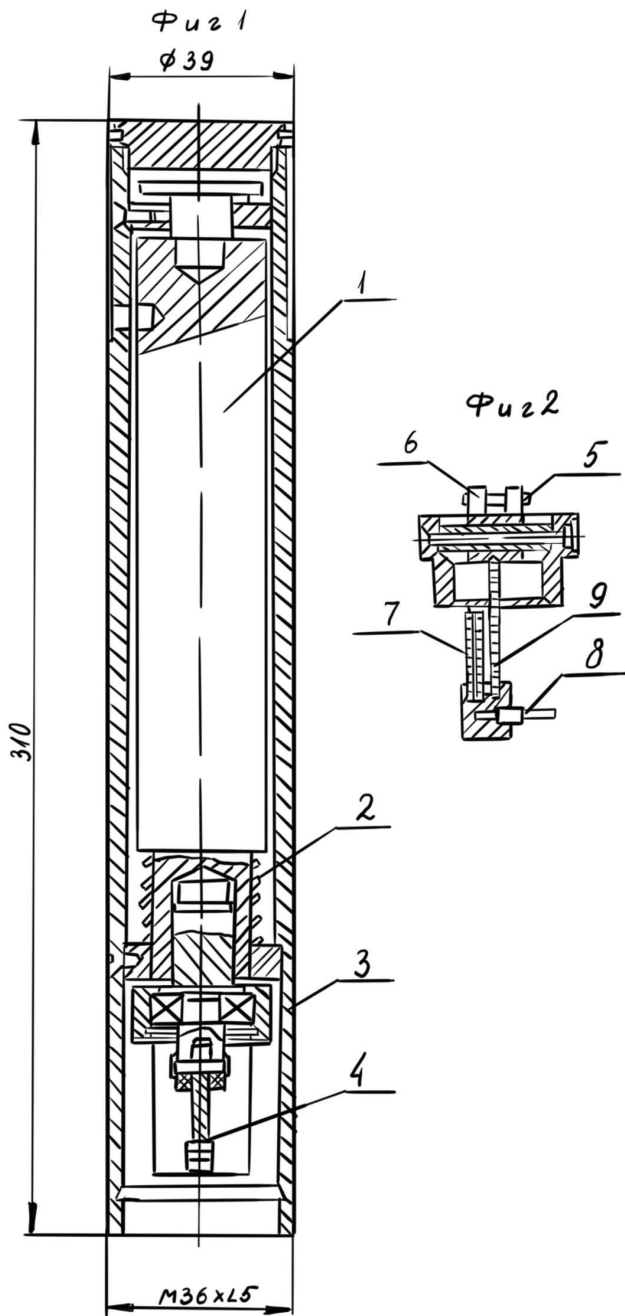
Датчик продольных колебаний. 1 — подвес, 2 — пружина винтовая, 3 — корпус, 4 — коромысло, 5 — ось, 6 — рычаг, 7 — трубка, 8 — электромагнитическая головка, 9 — пружина плоская
